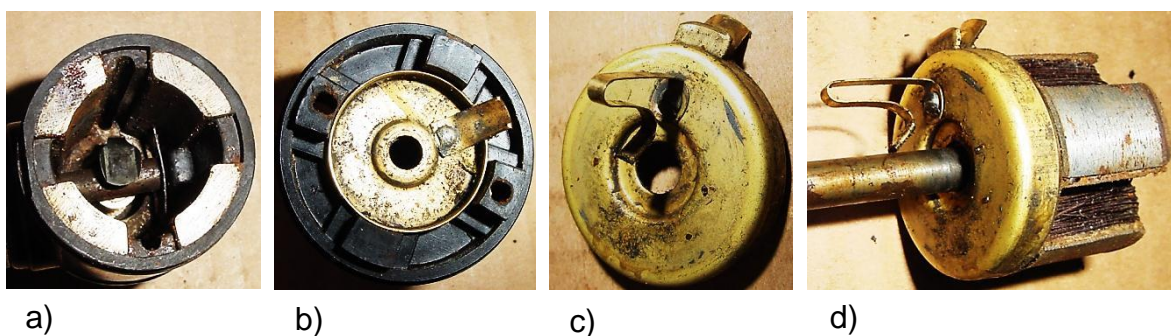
Massekontaktstellen: a) Rechteckiges Kontaktblech zwischen dem Drehbolzen und zwei Stabmagneten, b) Blechkralle zwischen dem Kontaktteller und einem Stabmagneten, c) Federbürsten für die Verbindung der Welle mit dem Kontaktteller, d) Position des Kontakttellers oberhalb des Anker
